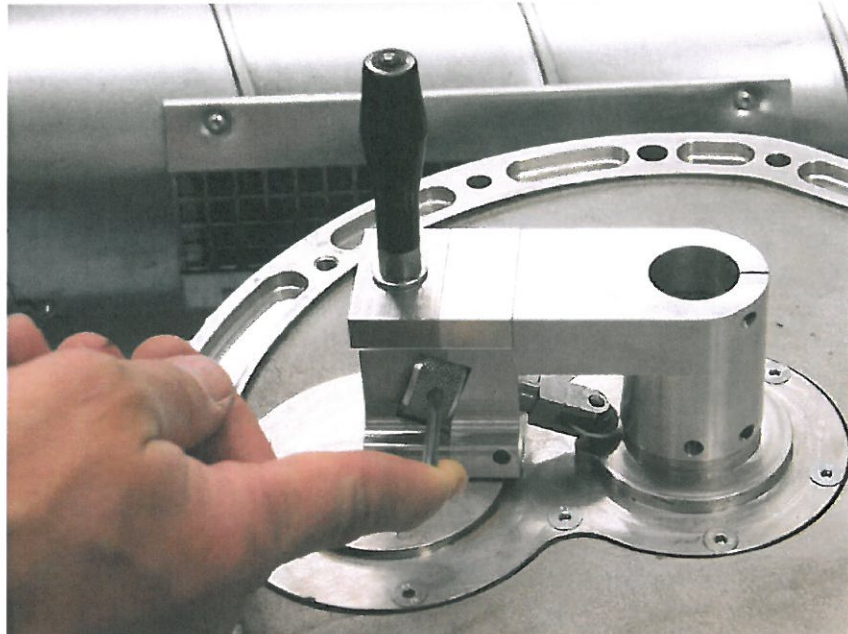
Das Schneidwerkzeug am Einstellrad zustellen
